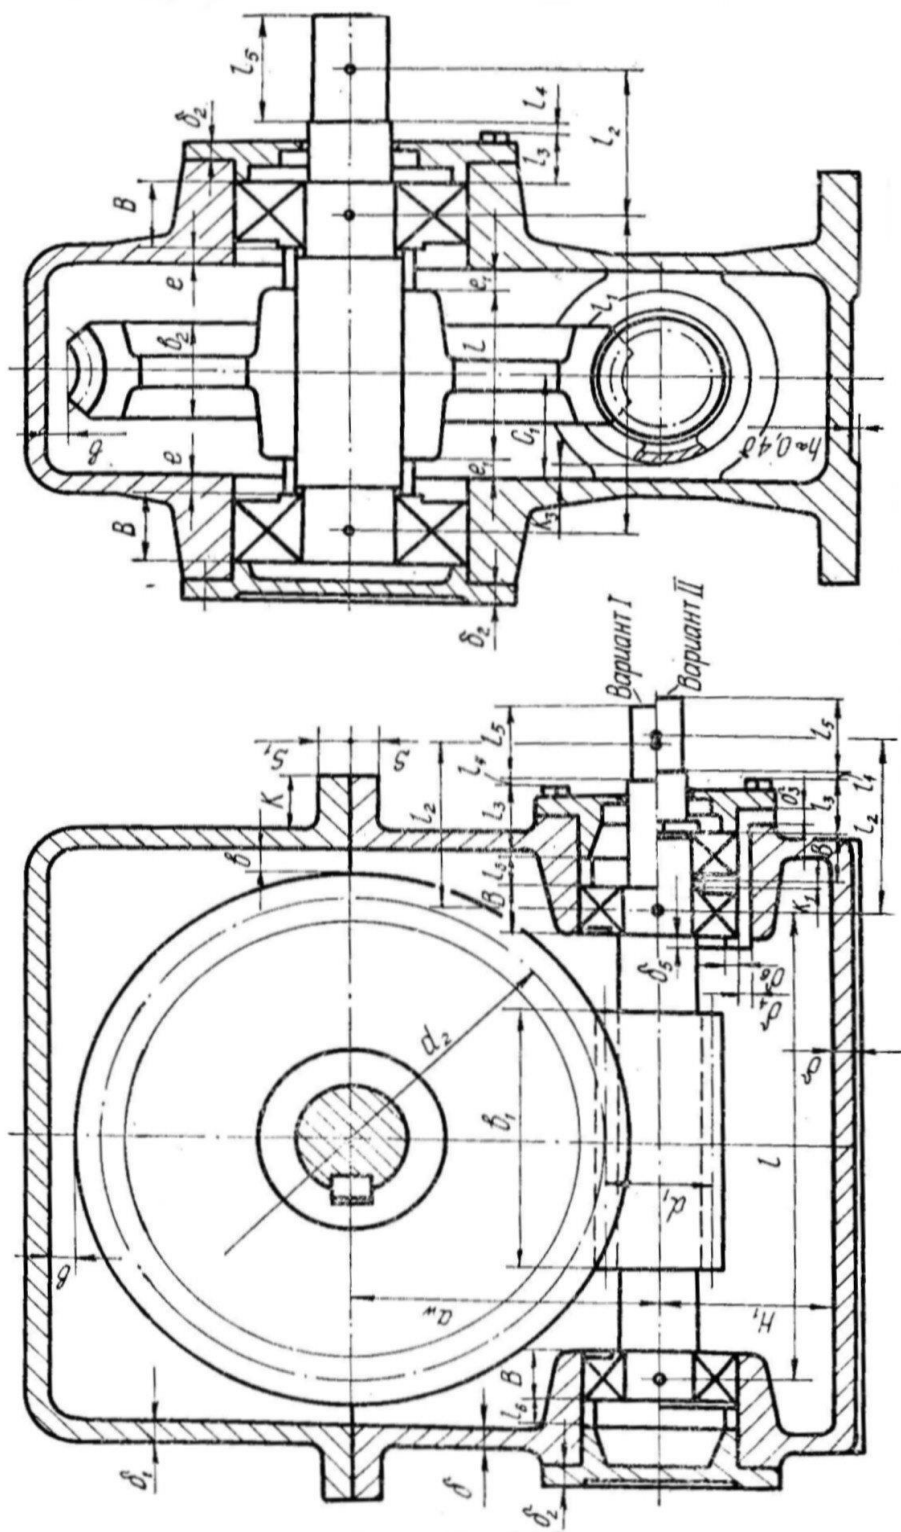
Компоновочне креслення черв'ячного редуктора
